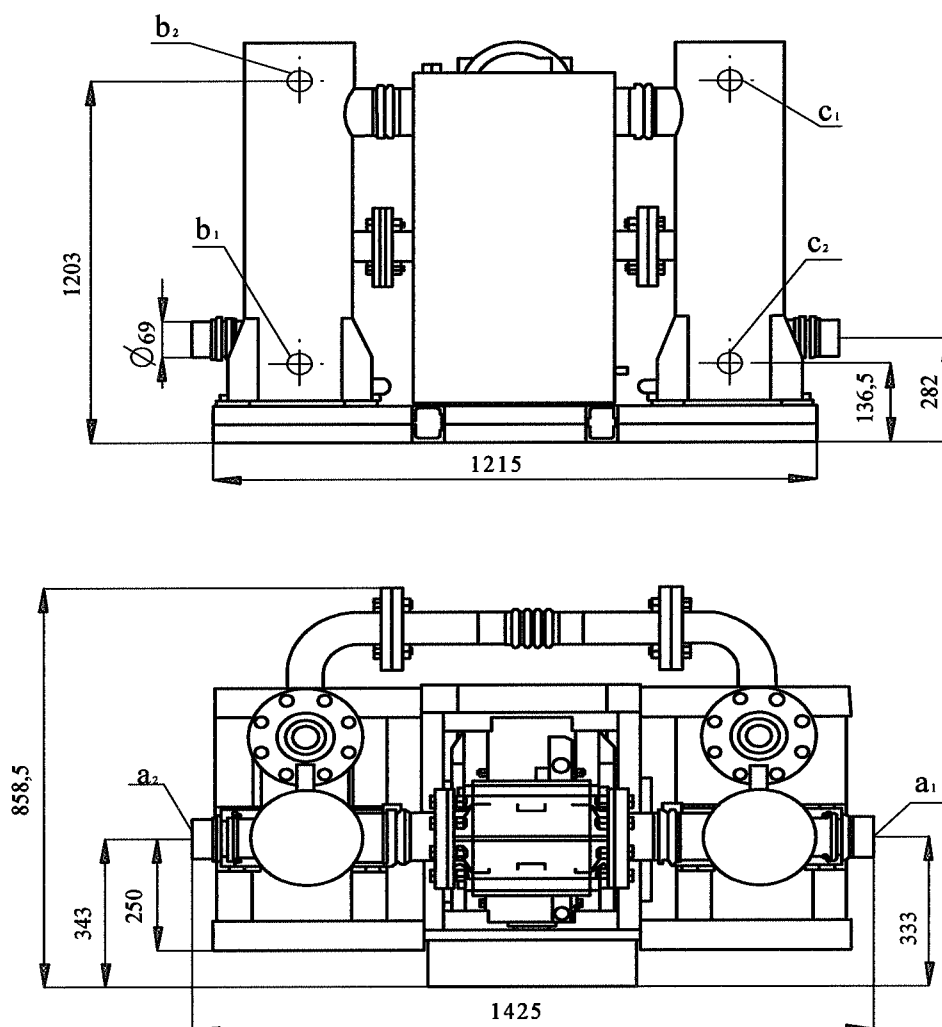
Габаритный чертеж компрессора KPL11AN001, KPL12AN001, KPL70AN001, KPL70AN002
